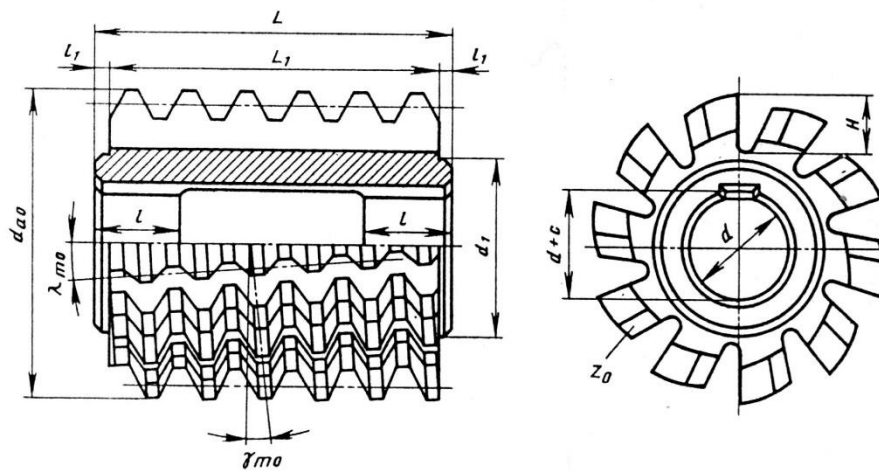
Конструктивні та геометричні параметри фрези [5]
